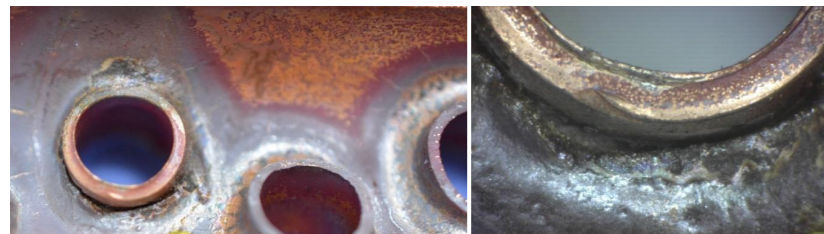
Příklad trhlin v koutovém pájeném spoji
